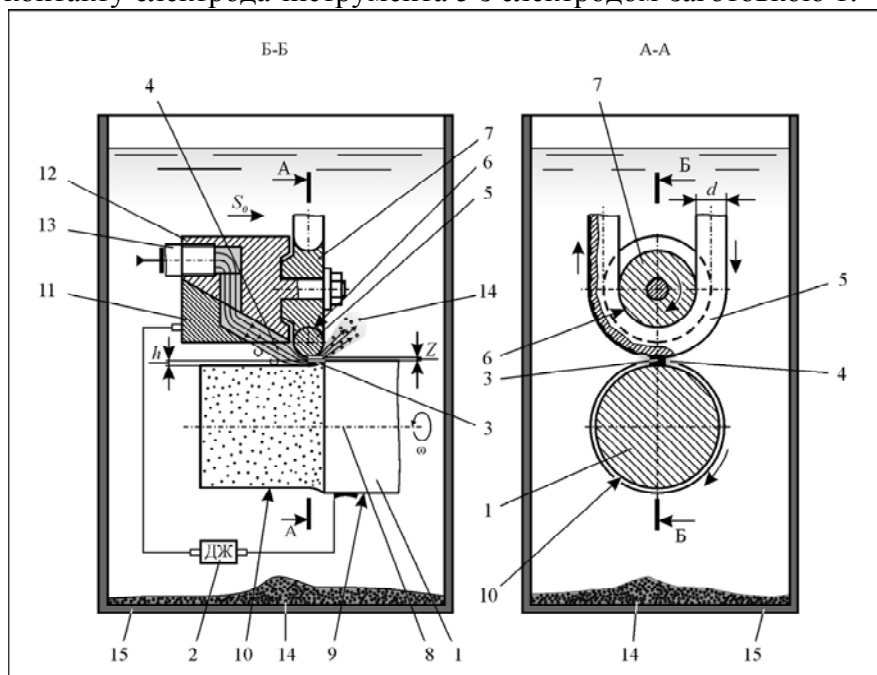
Принципова схема пристрою для реалізації технологічної схеми формоутворення поверхні тіла обертання електричною дугою з використанням дротового електрода-інструмента та зануренням зони обробки в робочу рідину
